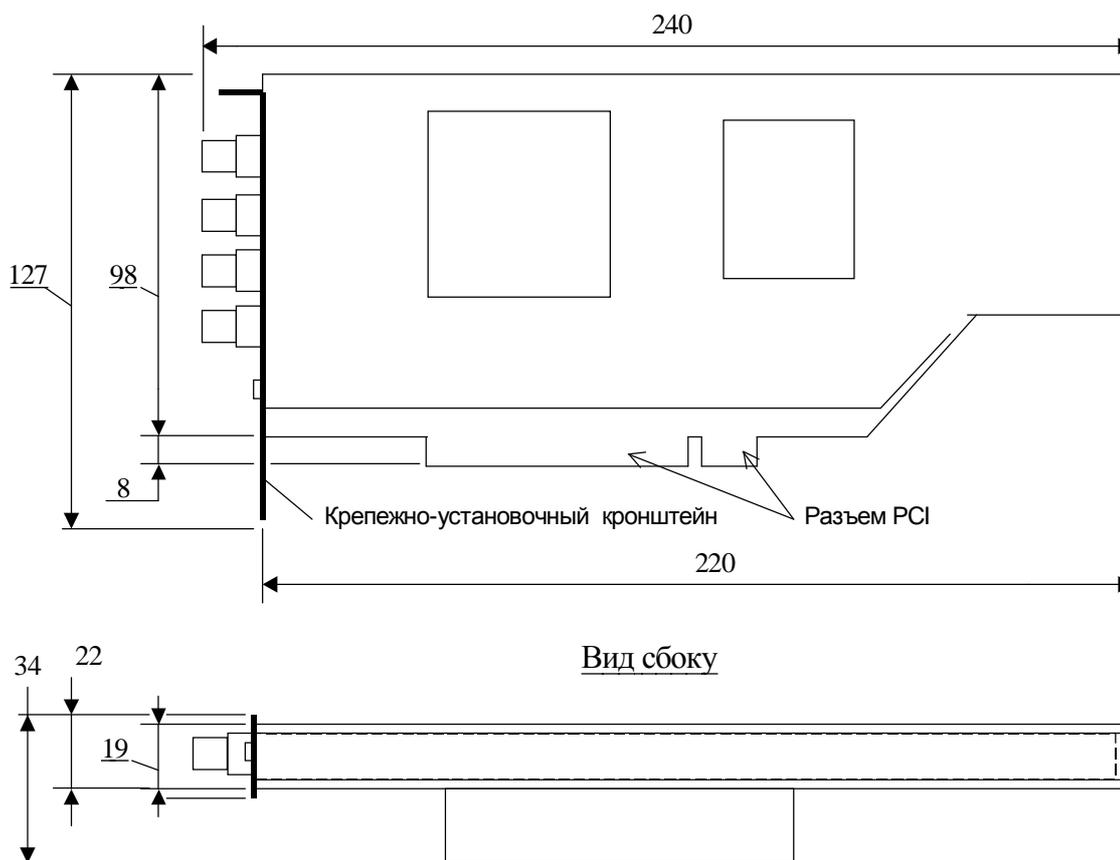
Габаритные размеры платы ЛА-н10м8РСІ-0108-500
